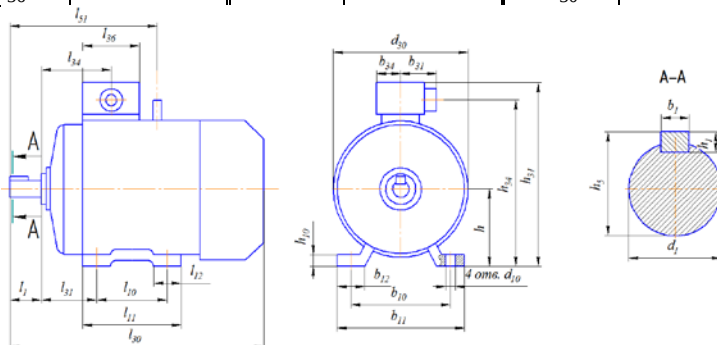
Габаритные, установочно-присоединительные размеры
